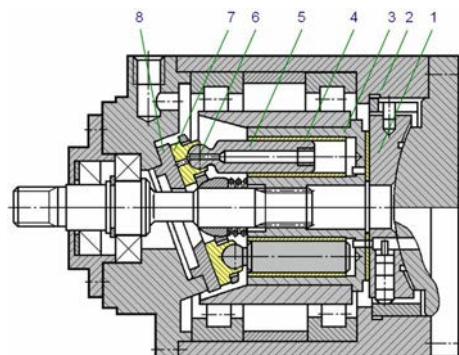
Принципиальная схема испытываемого гидронасоса: 1 – распределительный диск; 2 – статор; 3 – ротор; 4 – втулка цилиндра; 5 – поршень; 6 – сфера поршня; 7 – башмак; 8 – покатая шайба
